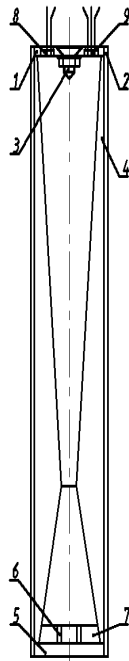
Схема ТТ: 1-верхняя крышка; 2-цилиндрический корпус ТТ; 3-конический турбулизатор; 4-капиллярно-пористая вставка; 5-нижняя крышка; 6-инжекторные каналы; 7-капиллярно-пористый испаритель; 8,9-емкостные датчики конденсации, измеряющие толщину слоя жидкого конденсата.
